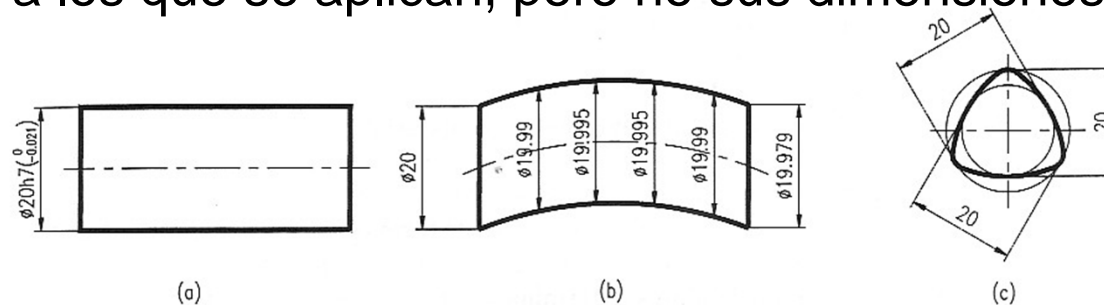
(a) Especificación de tolerancias dimensionales en un cilindro. (b) Dimensiones de una pieza fabricada con errores de rectitud. (c) Dimensiones de una pieza fabricada con defectos de redondez.
